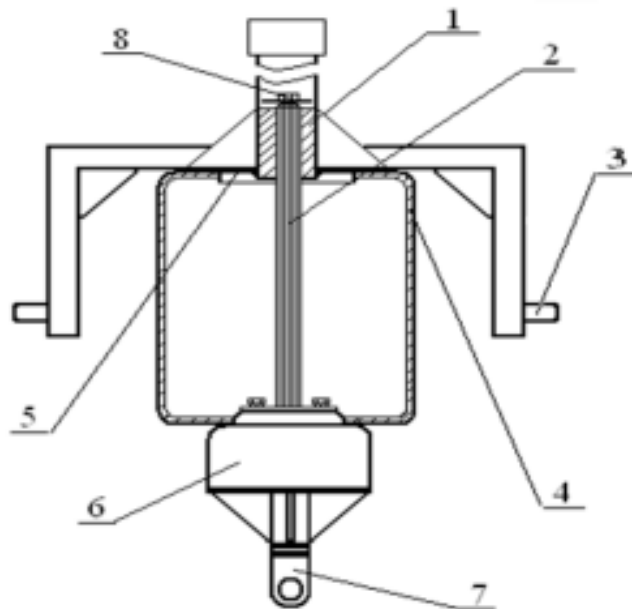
Схема пневматичного запобіжника: 1 – втулка; 2 – шліцьовий вал (напрямна); 3 – верхні опорні вушка; 4 – пневматична камера; 5 – верхня опорна пластина; 6 – додаткова камера; 7 – фланець; 8 – обмежувальний болт.
